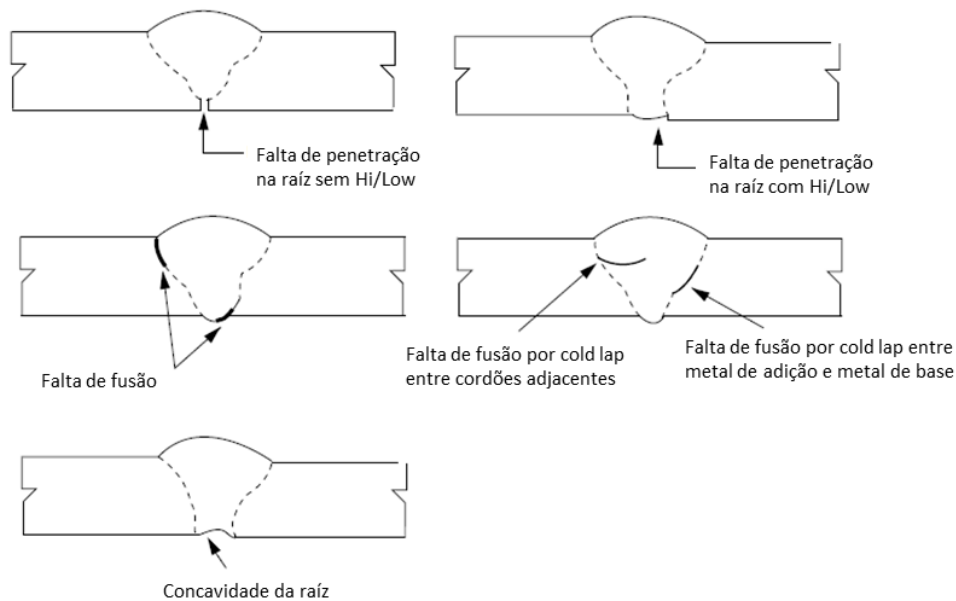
Defeitos de soldagem (adaptado de API 1104)
